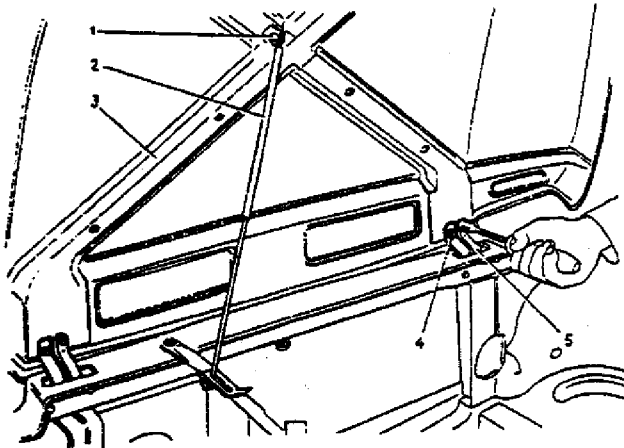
Fixação do capuz: 1 - eixo de articulação do suporte; 2 - suporte; 3 - capuz; 4 - parafuso de fixação das dobradiças; 5 - dobradiças.
